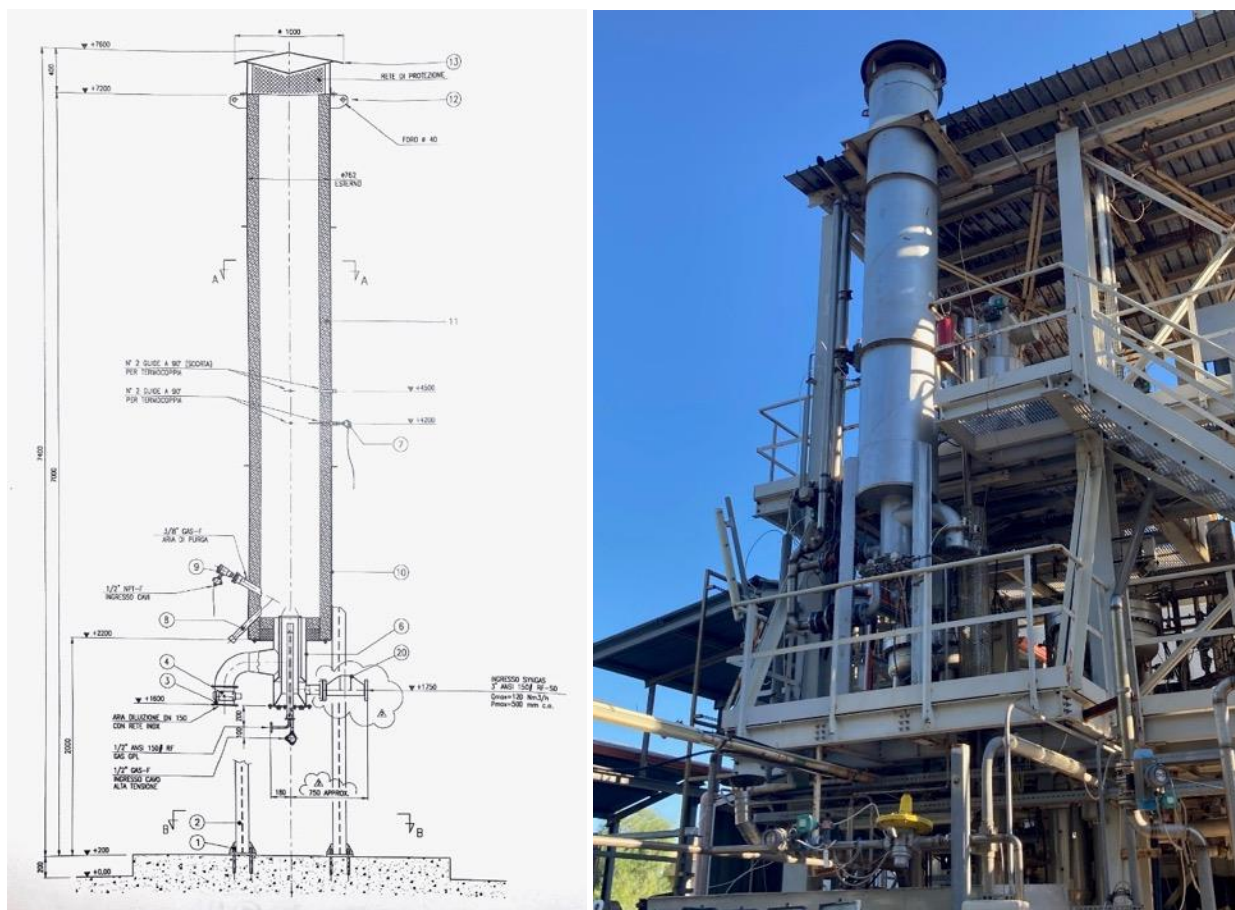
Disegno di assieme e foto della torcia installata sull'impianto.
